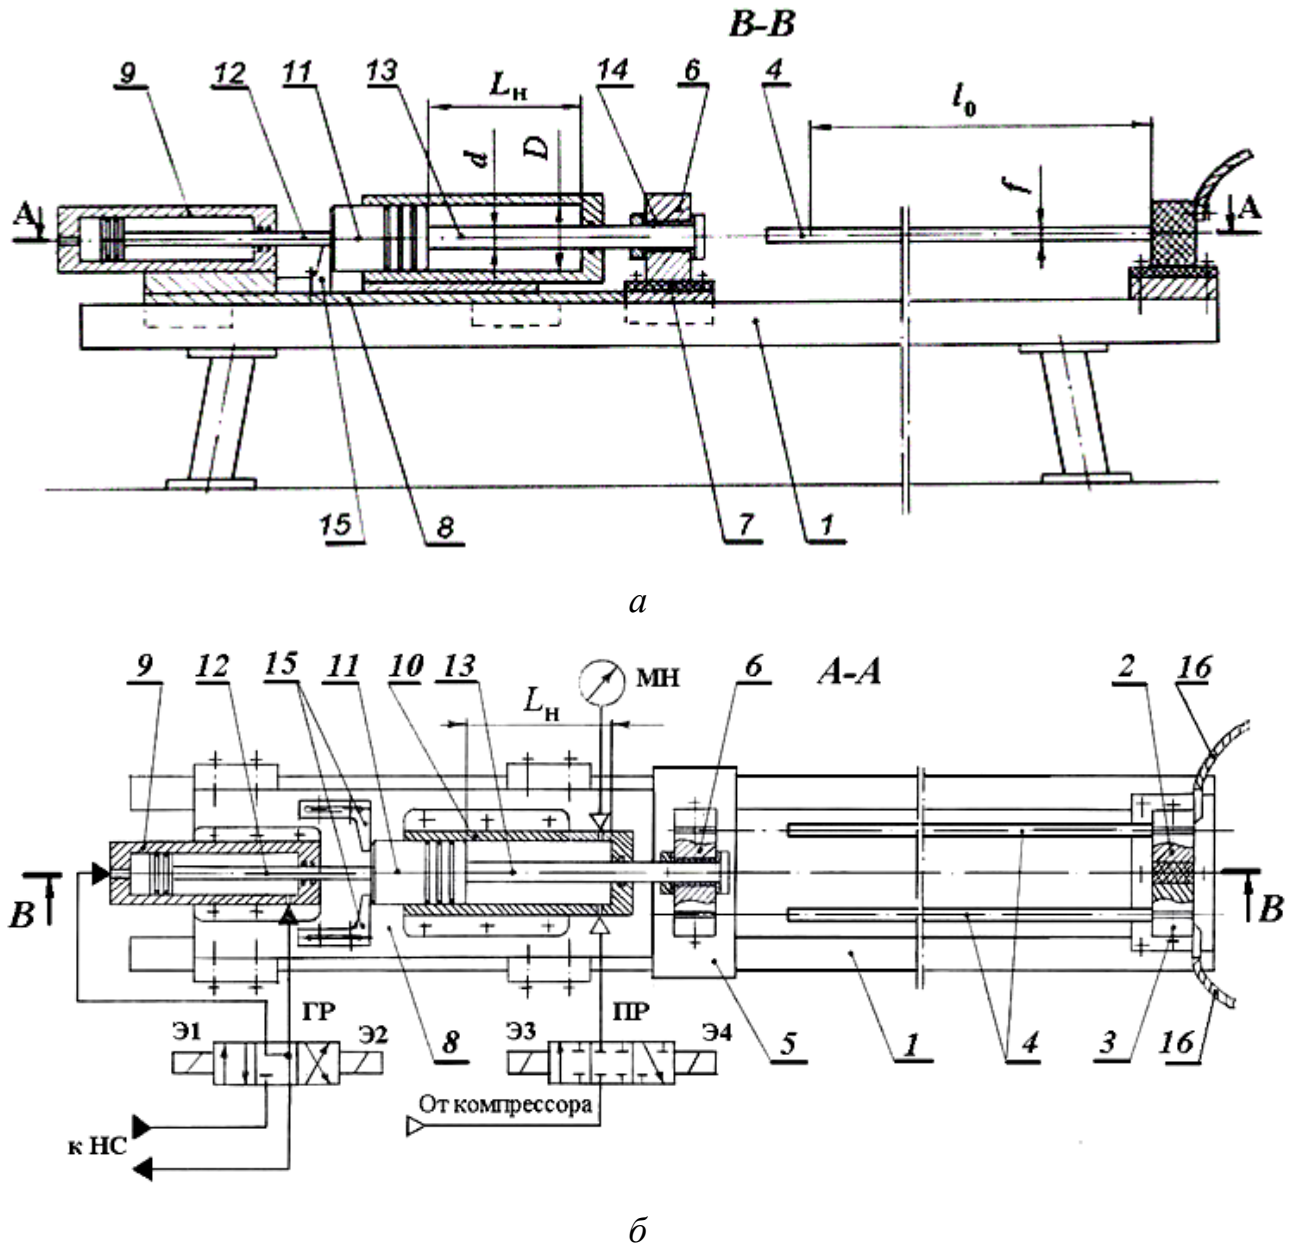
Конструктивная схема установки: *а* – продольный вертикальный разрез В-В установки; *б* – продольный горизонтальный разрез А-А установки в исходном состоянии: 1 – станина; 2 – неподвижные контакты, 3 – прижимы; 4 – труба; 5 – суппорт; 6 – подвижный контакт; 7 – изоляционная прокладка; 8 – платформа; 9 – поршневой гидроцилиндр; 10 – плунжерный пневмоцилиндр; 11 – плунжер; 12 – шток гидроцилиндра, 13 – шток пневмоцилиндра; 14 – фланцевая втулка; 15 – упоры, 16 – клеммы вторичной обмотки
